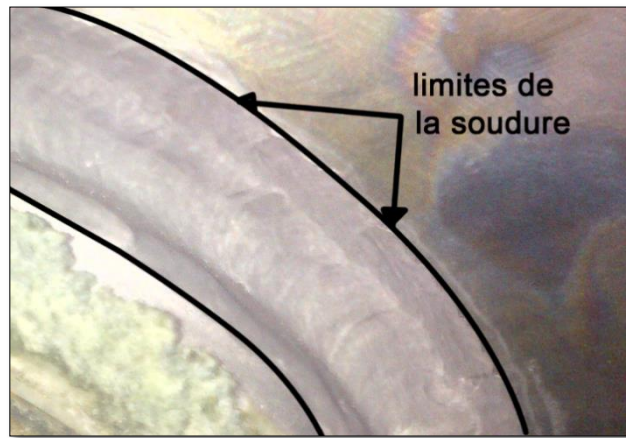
état de surface de la soudure entre le moyeu et la roue centrifuge (307/C08)
